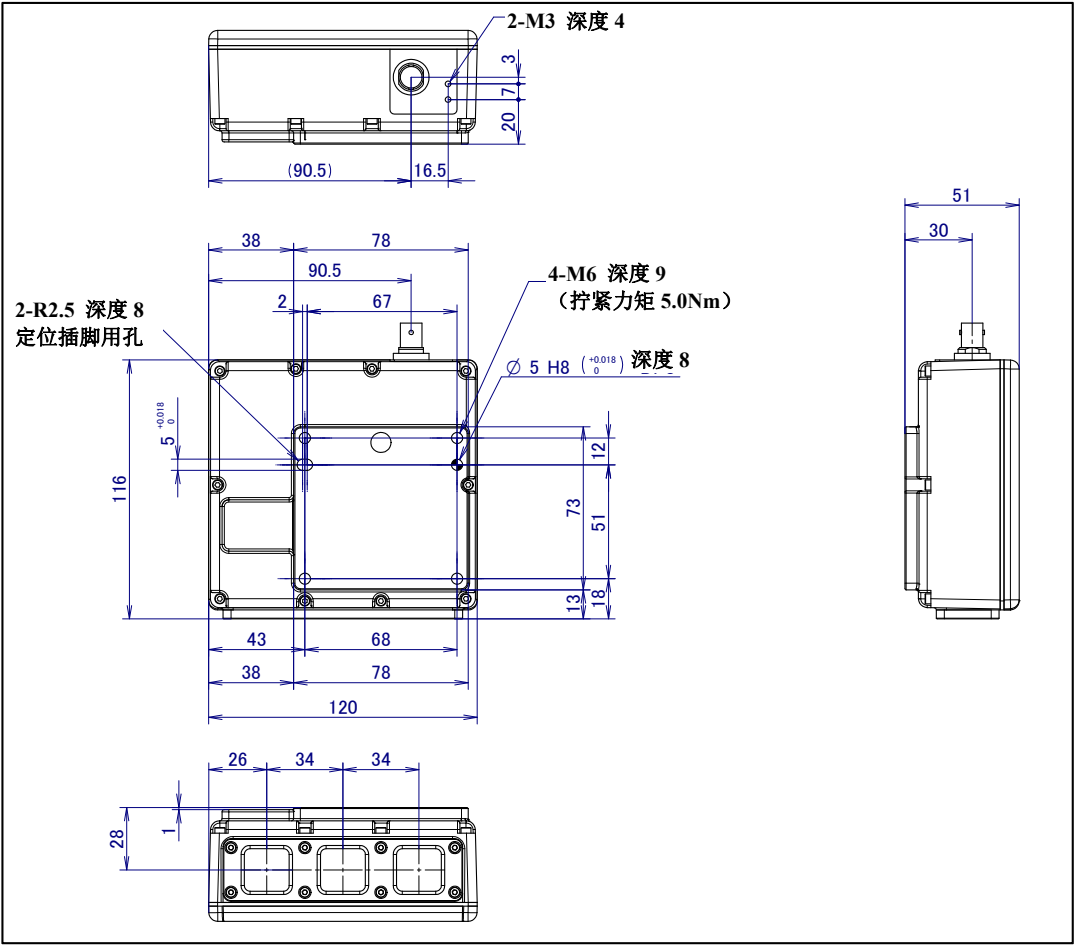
(b) 3D 视觉传感器外形尺寸 (3DA/400, 没有 LED)
